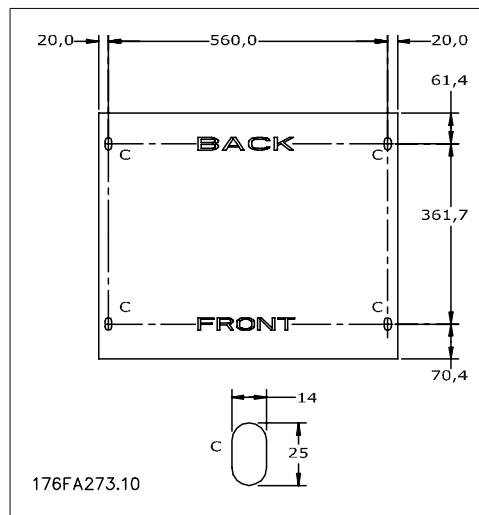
Чертеж для сверления крепежных отверстий в полу.
